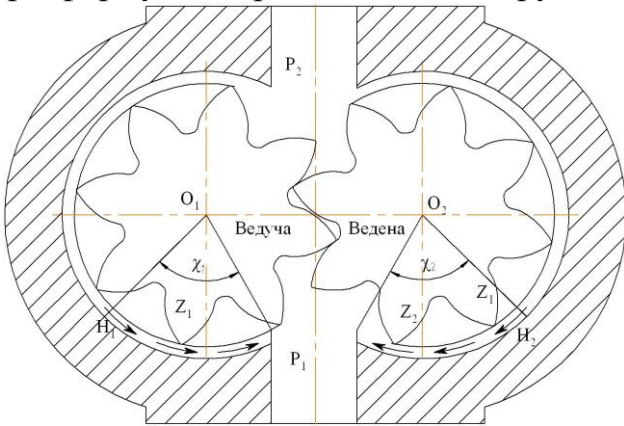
Схема витоків через радіальний зазор. Момент роботи НШ, при якому радіальний зазор ведучої шестерні формується одним зубцем, а веденої – двома зубцями
